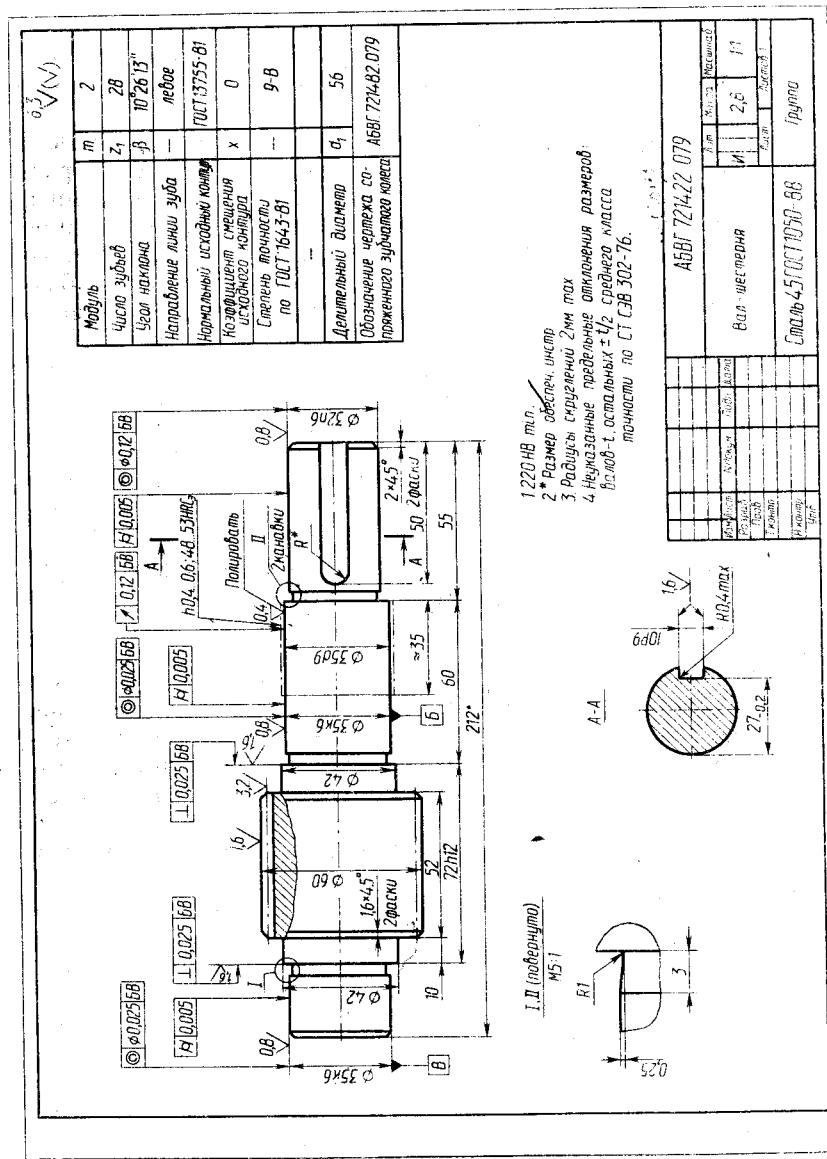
Пример рабочего чертежа вала-шестерни цилиндрической
